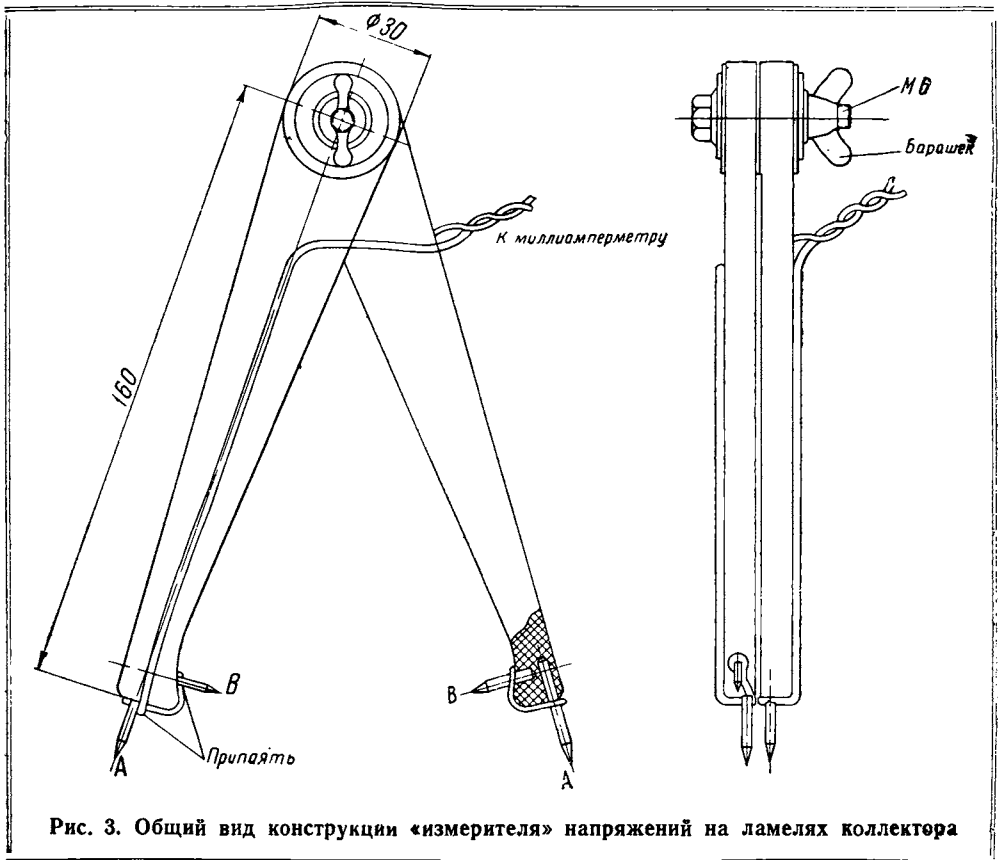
Общий вид конструкции «измерителя» напряжений на ламелях коллектора
